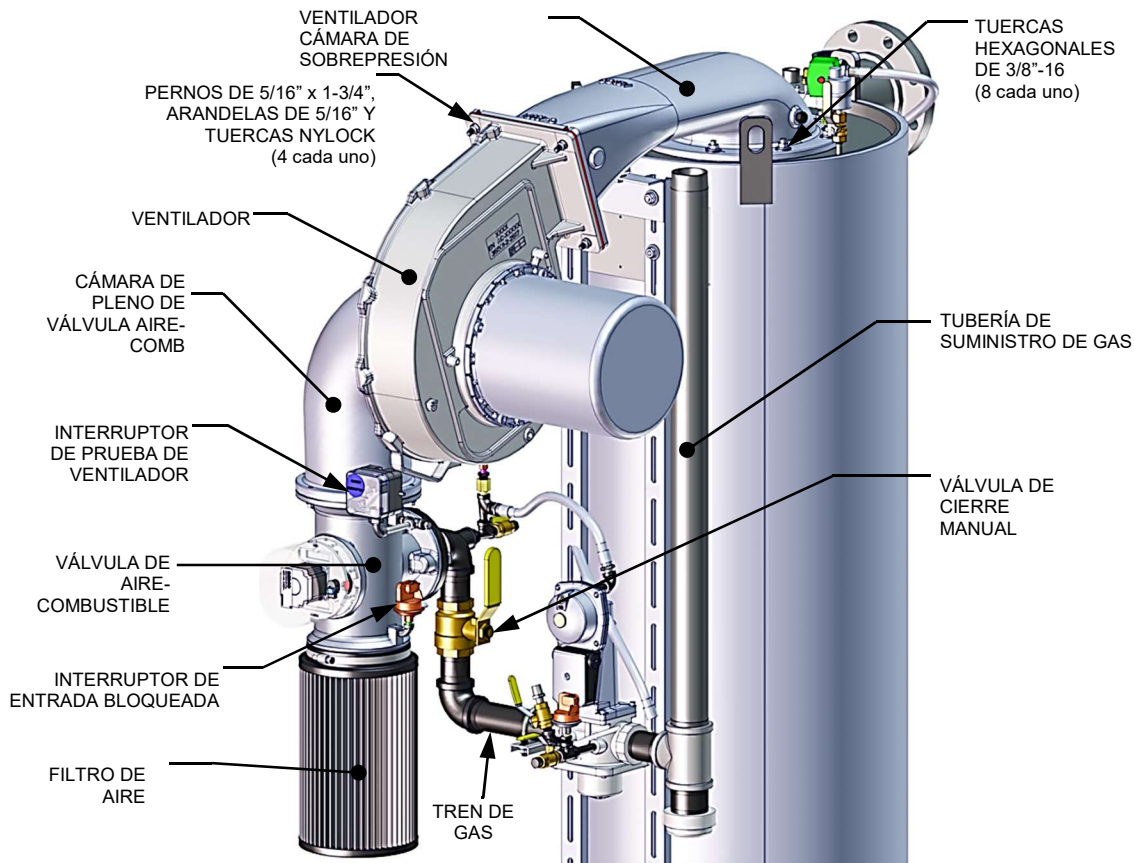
Información de montaje de ensamblado del quemador de BMK 2500/3000
